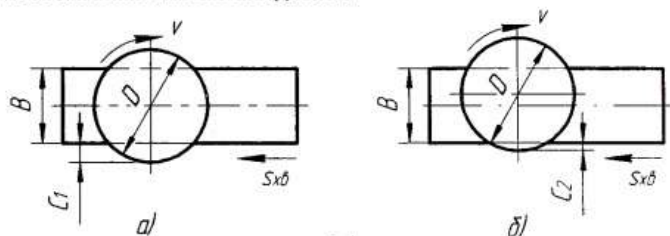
Розташування сталевій заготовці щодо фрези (торцеве фрезерування):
